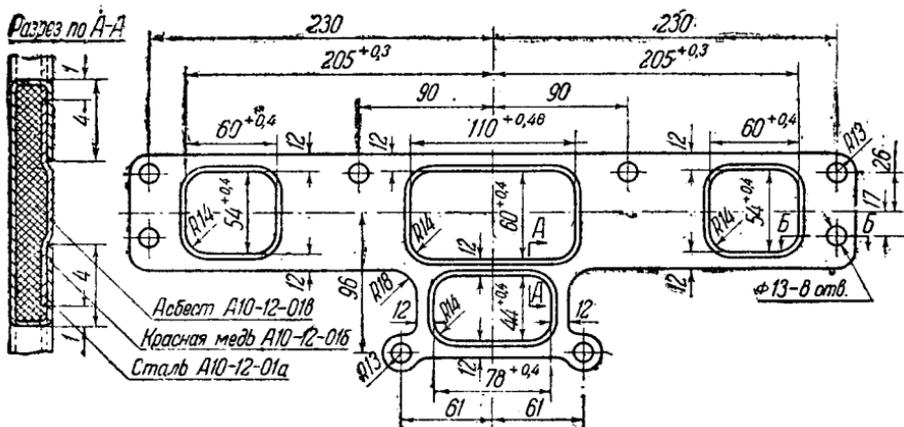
Дет. А08-3. Прокладка корпуса масляного радиатора
